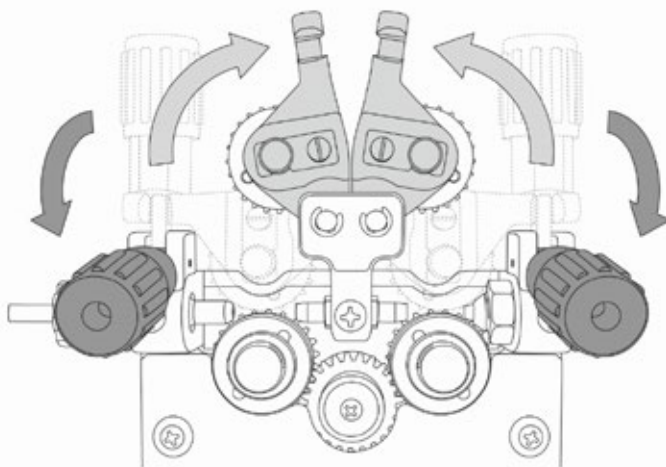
Подготовка сварочной проволоки.
